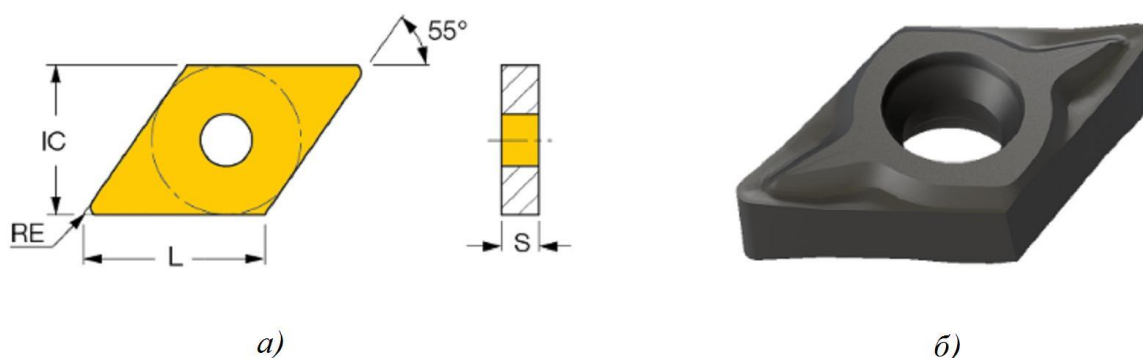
Пластина расточная чистовая [1]: а- схема; б - общий вид
